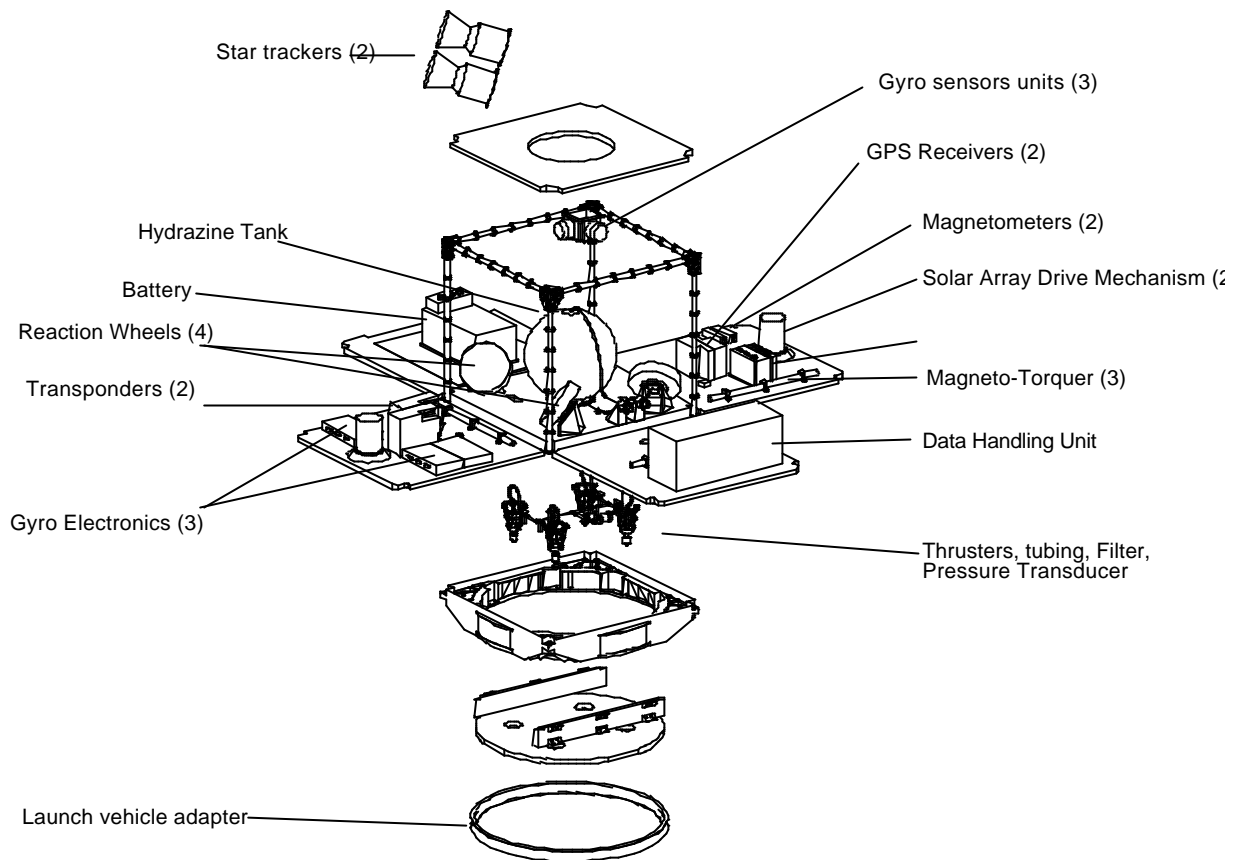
Vue éclatée de la plate-forme PROTEUS
